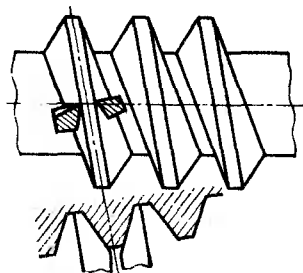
Схема установки двустороннего резца для нарезания витка червяка ZN2
